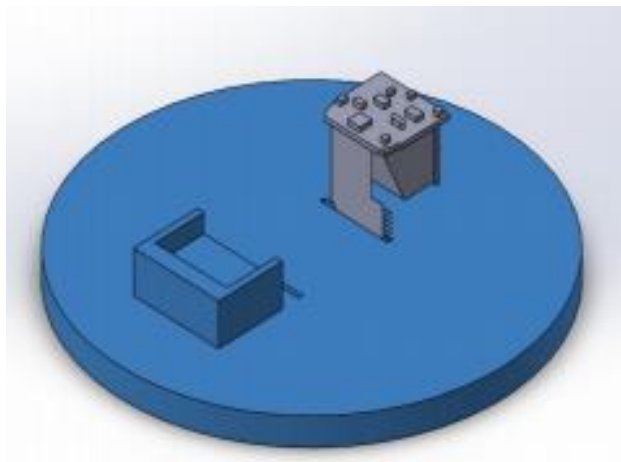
Fixture para operación de soldadura de L Flex, con Detector de Mainstream, vista 1.
